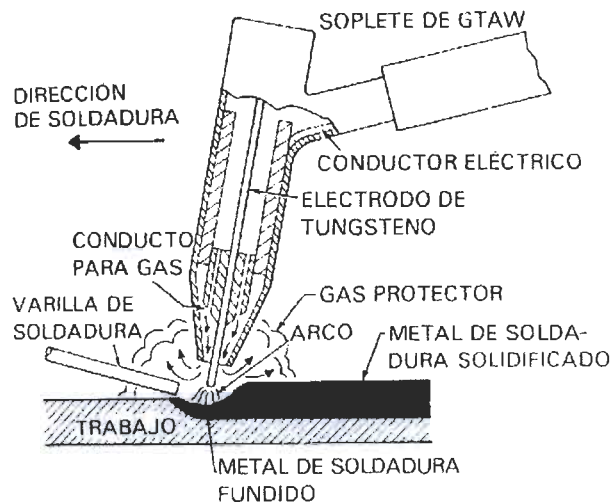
Proceso de soldadura GTAW (15).
